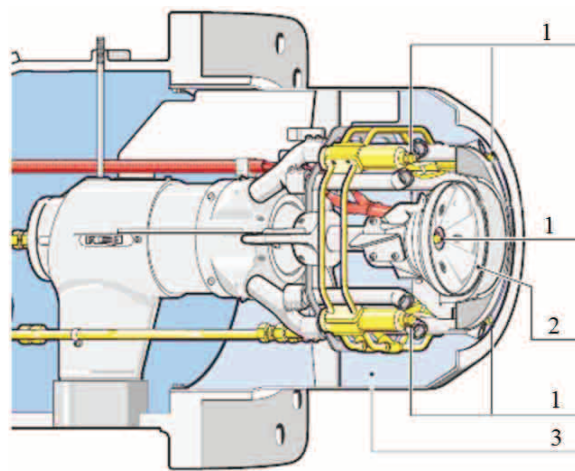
Конструктивная схема исследуемой горелки [25]: 1 – форсунки подачи синтез-газа; 2 – каналы подачи первичного воздуха; 3 – канал подачи вторичного воздуха
